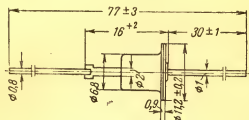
Габаритный чертеж диодов Д217, Д218.
